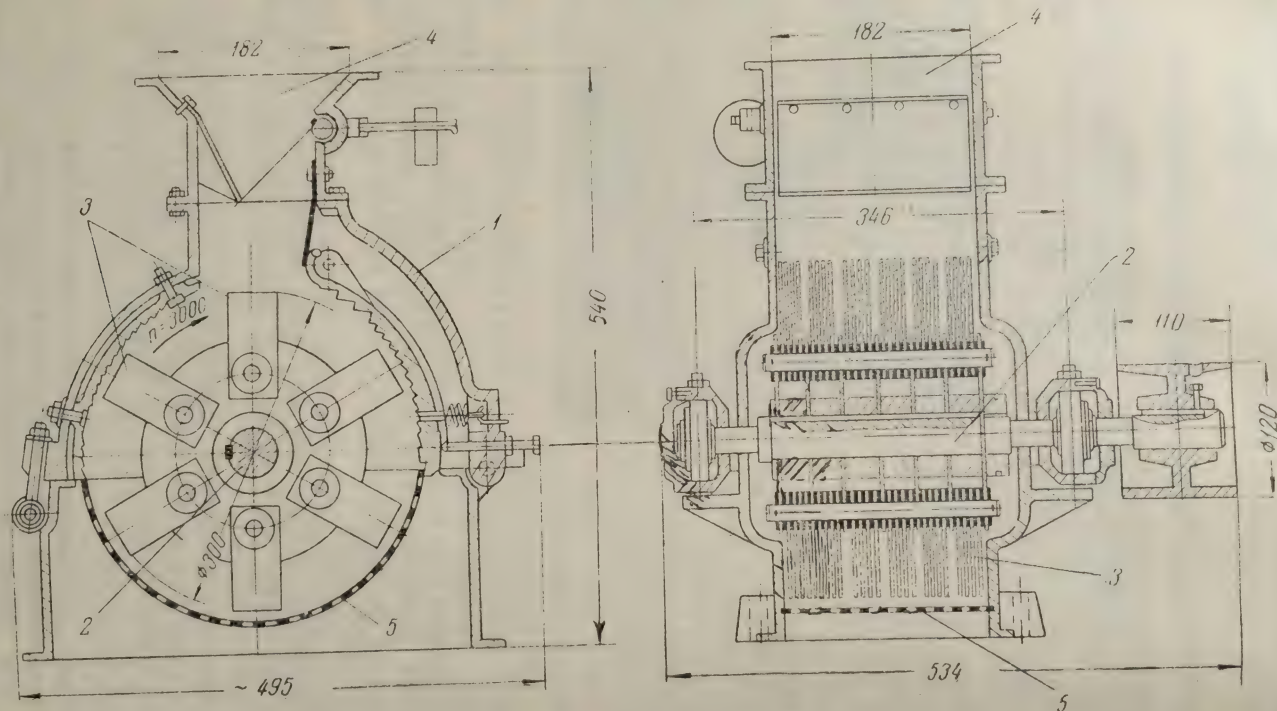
Дробилка для шквары и кости типа ДМ-300:
